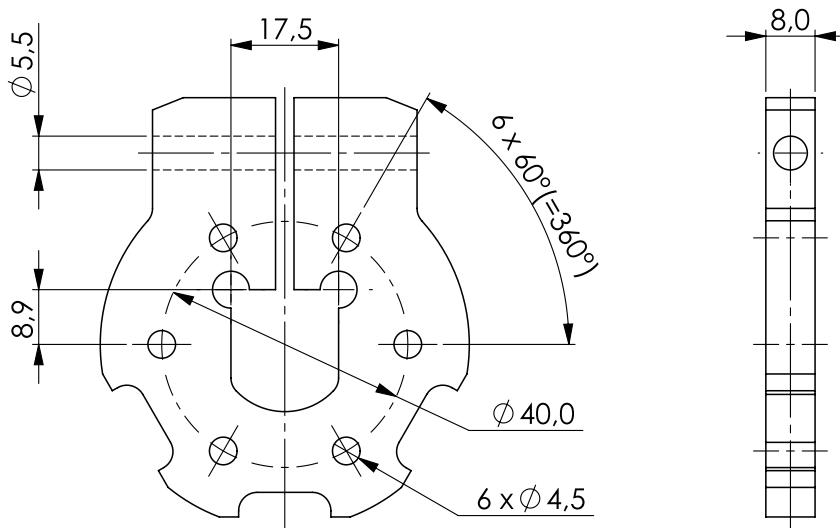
Zeichnung des Gegenstücks der Zahnscheibe um eine ebene Fläche für die Muttern zur Verfügung zu stellen.
